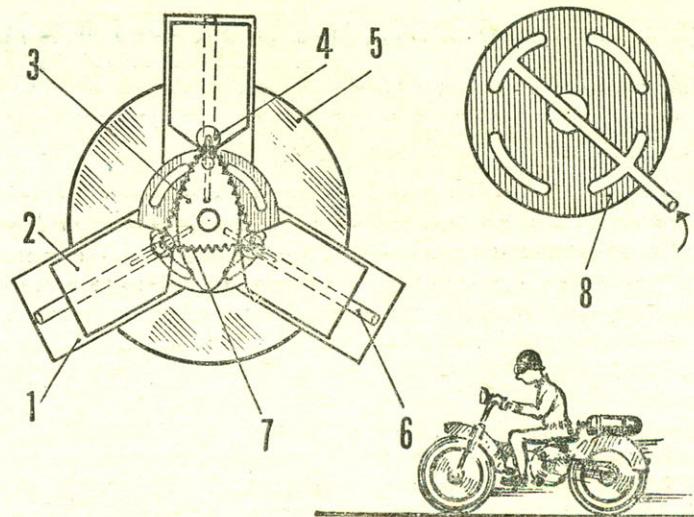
Схема кулачково-поршневого двигателя с вращающимися цилиндрами:
